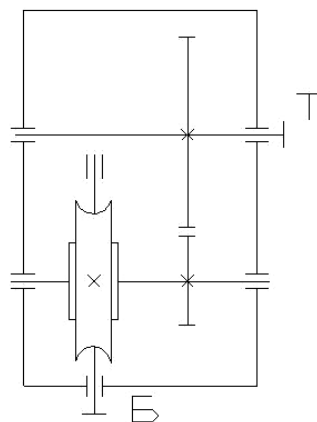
Двухступенчатый червячно-зубчатый редуктор
